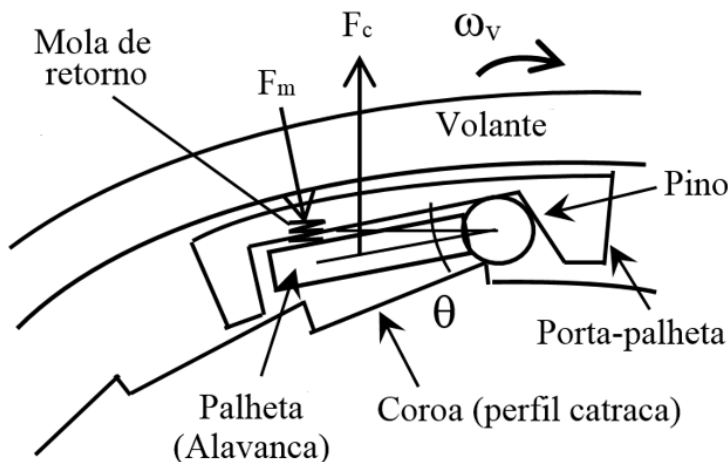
Perfil da catraca, conforme projeto detalhado do sistema.
